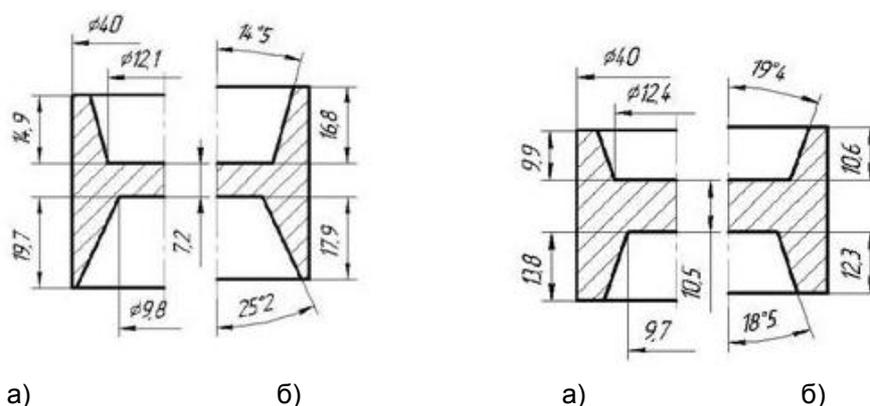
Размеры выдавленных деталей двух типоразмеров:
